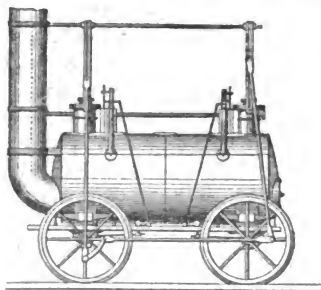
Machine à bielle d'accouplement de Stephenson.
